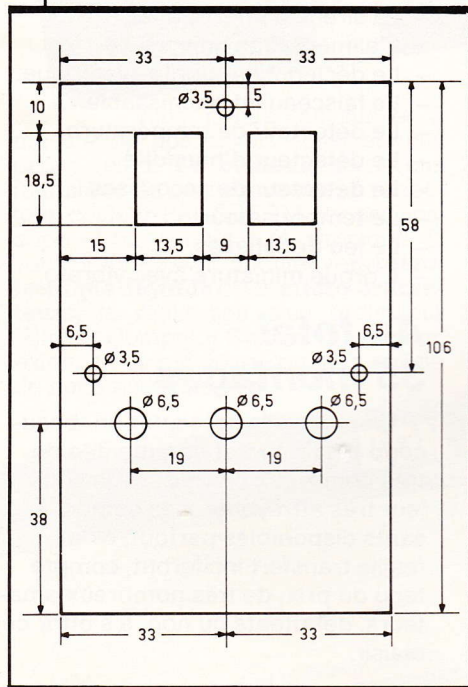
Plan de découpe de la face avant du coffret Teko.
